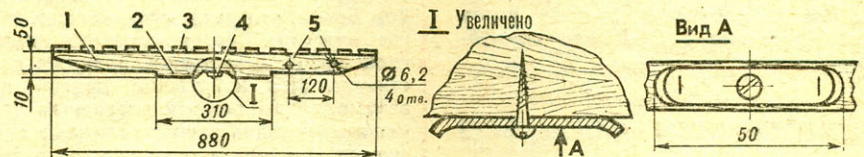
Грузовая платформа: 1 — продольный силовой брус (2 шт.), 2 — выступ бруса, 3 — рейка настила, 4 — запор-вертушка, 5 — отверстия под болты крепления ручек.
